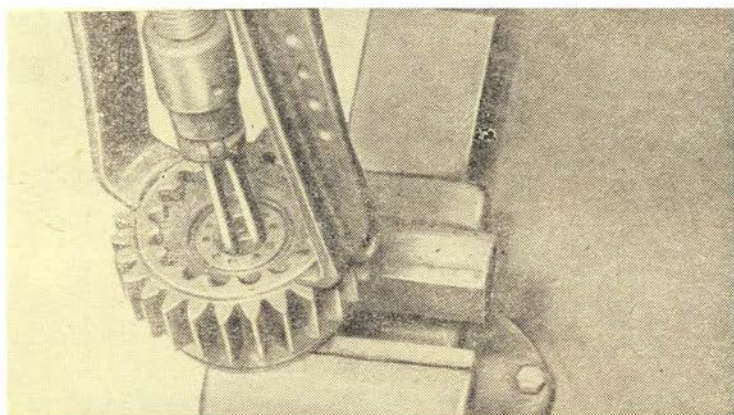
Выпрессовка из гнезда ведомого вала роликового подшипника
